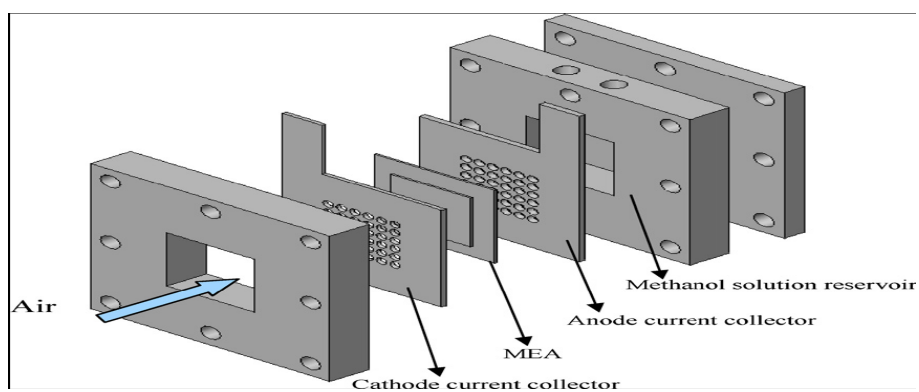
Pilha de Combustível, MEA - Membrane and Electrode Assembly. [40]
